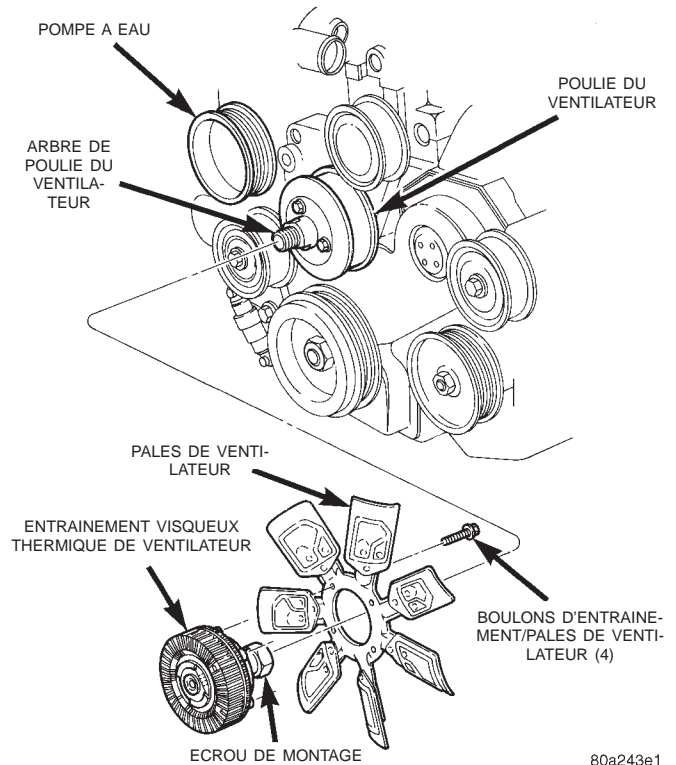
Ensemble d'entraînement/pales de ventilateur
